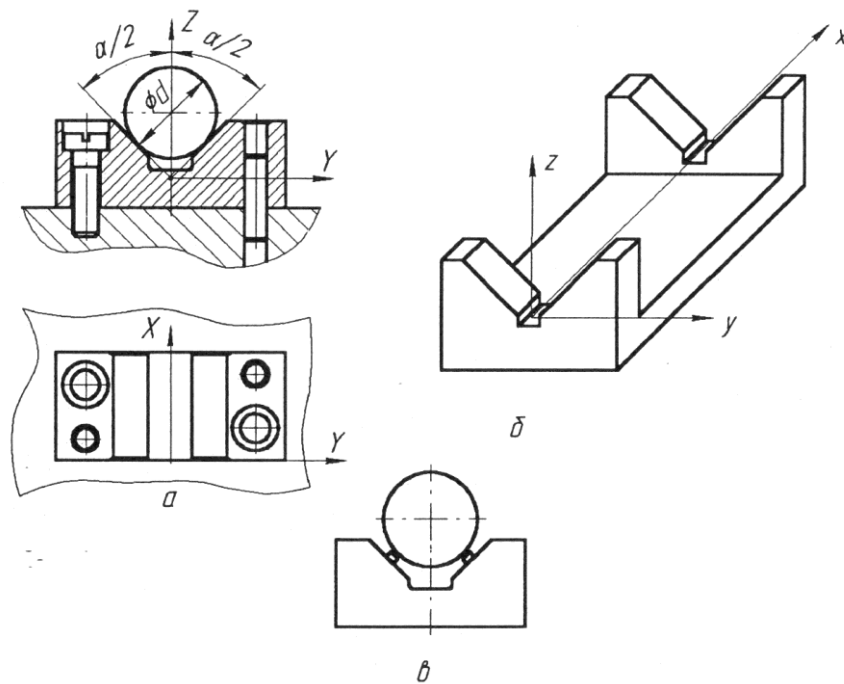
Призми: а - з широкими опорними поверхнями; б - з вузькими опорними поверхнями; в - з точковими опорами
